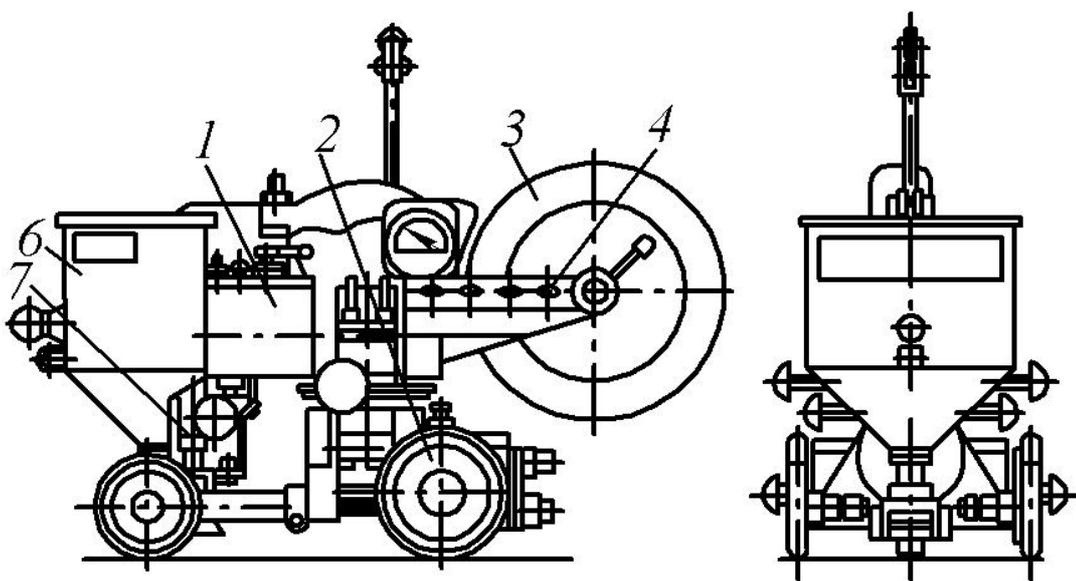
Загальний вигляд зварювального трактора ТС-35
